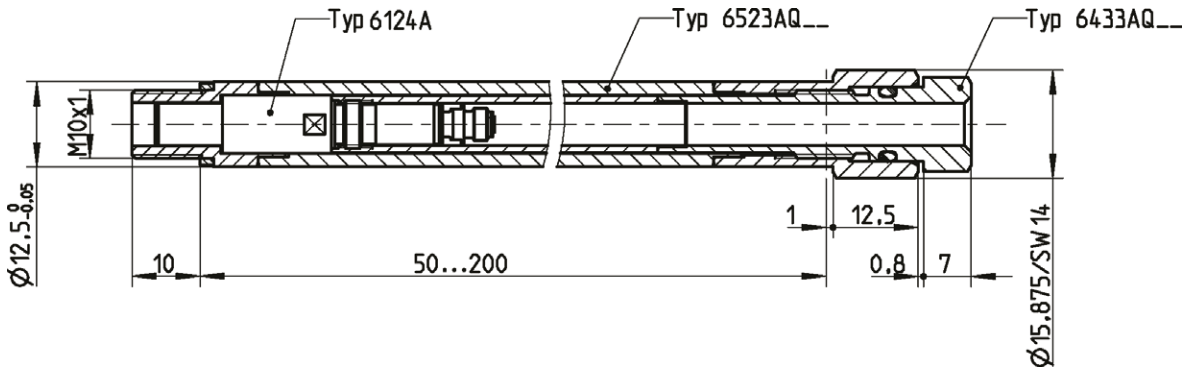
Montagehülse Typ 6523AQ mit M10x1 Druckstück Typ 6433AQ
